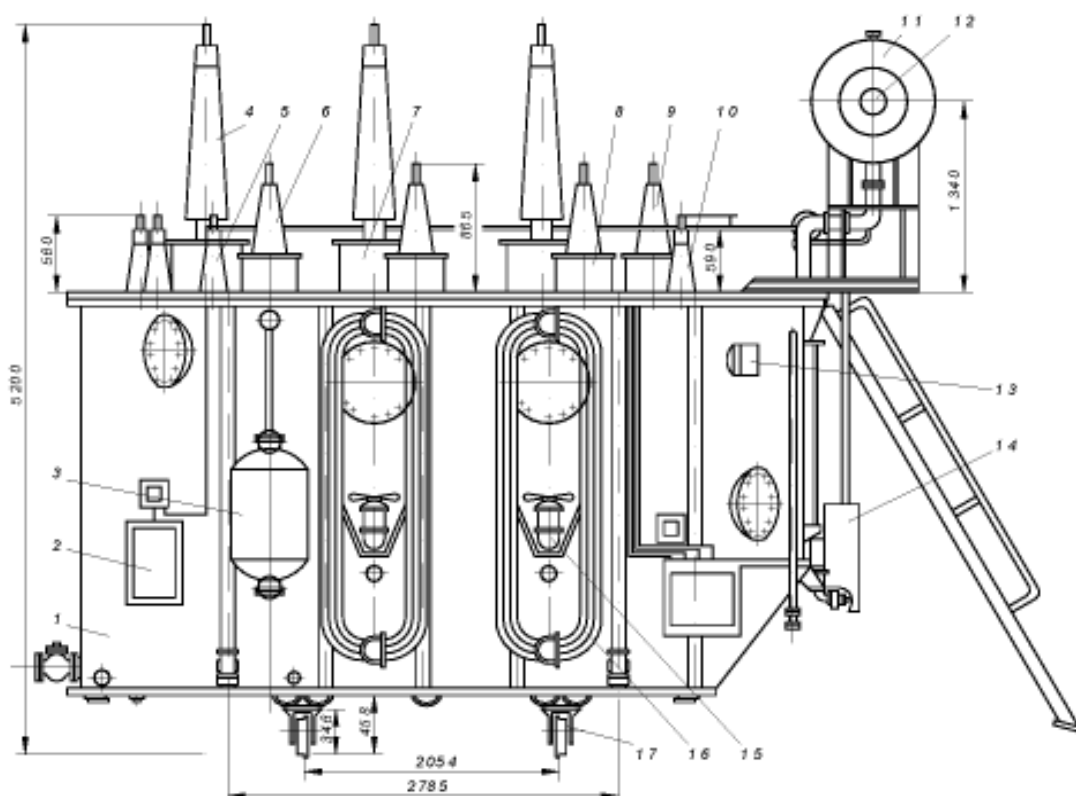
Трансформатор трехфазный трехобмоточный ТДТН-16000/ПО-80У1:1-бак; 2-шкаф автоматического управления дутьем; 3-термосифонный фильтр, 3-ввод ВН; 5- ввод НН; 6-ввод СН; 7-установка трансформаторов тока 110 кВ, 8-установка трансформаторов тока 35 кВ; 9-ввод О ВН; 10- ввод О СН; 11 - расширитель. 12-маслоуказатель стрелочный, 13-клапан предохранительный; 14-привод регулятора напряжения; 15-электродвигатель системы охлаждения; 16 - радиатор, 17 - каретка с катками
